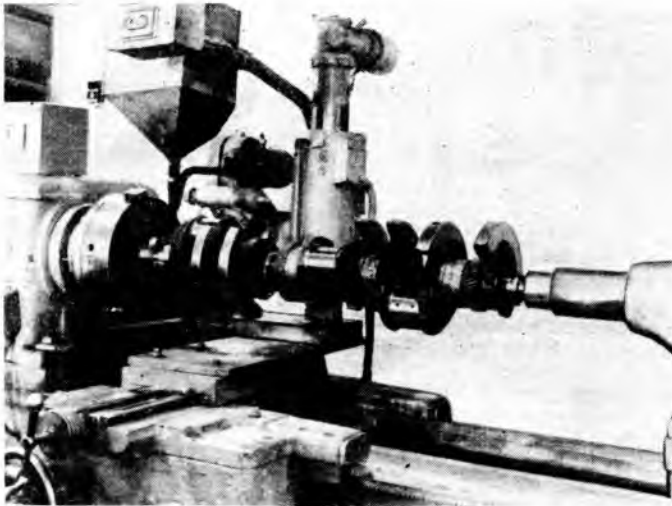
Наплавочная установка на базе токарно-винторезного станка модели 1Д63А
